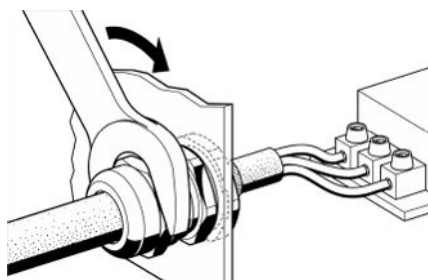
Накладання кабельних екранів на кабельні нарізні з'єднання EMC
